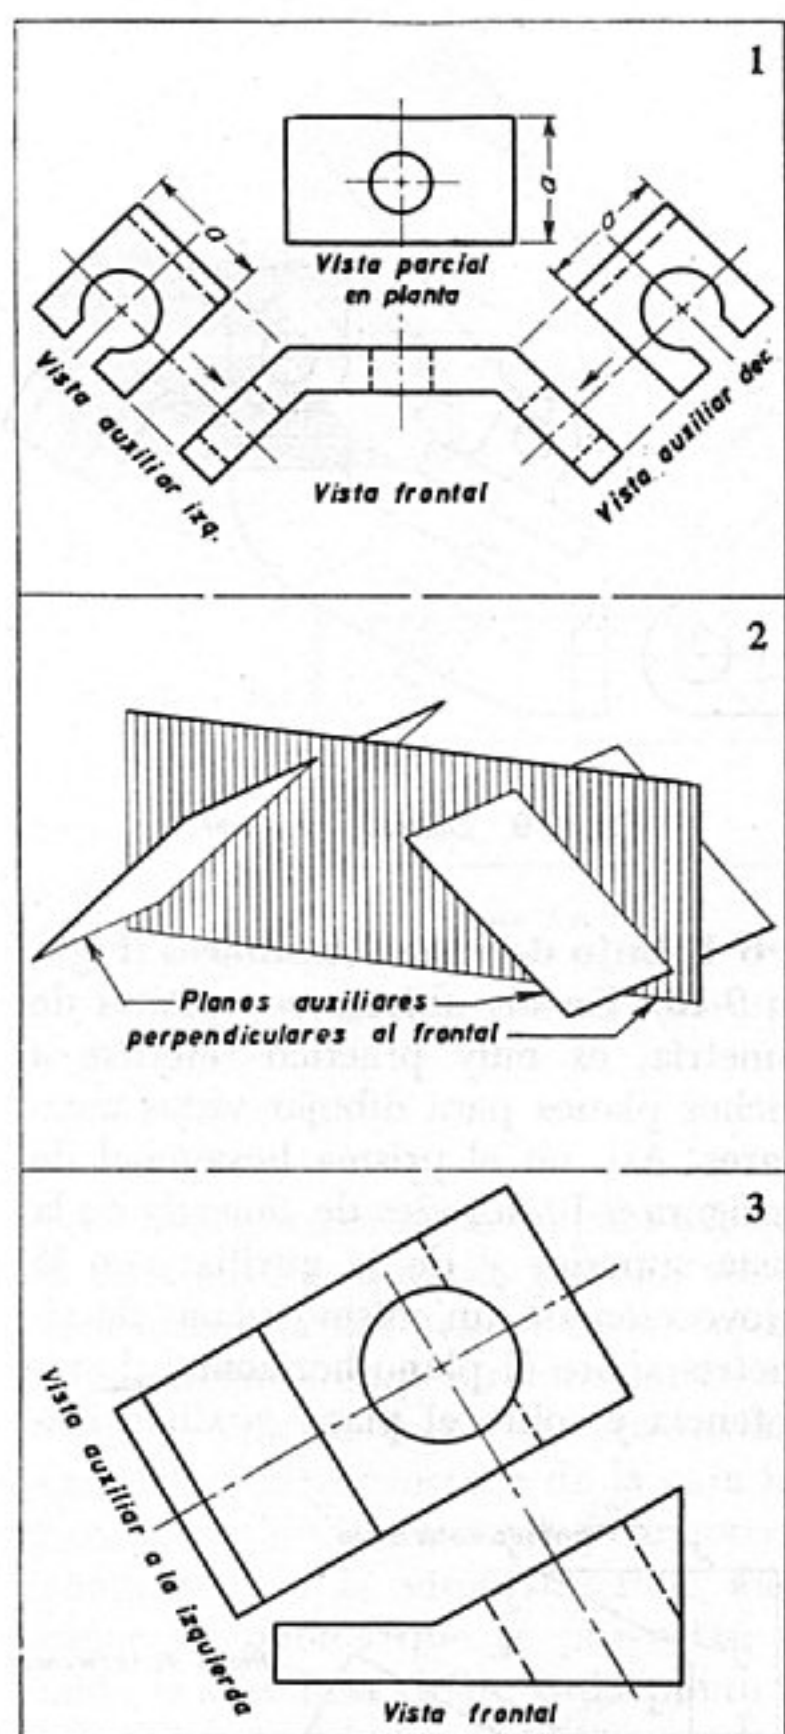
Vistas auxiliares a izquierda y a derecha, sobre planos perpendiculares al frontal.
